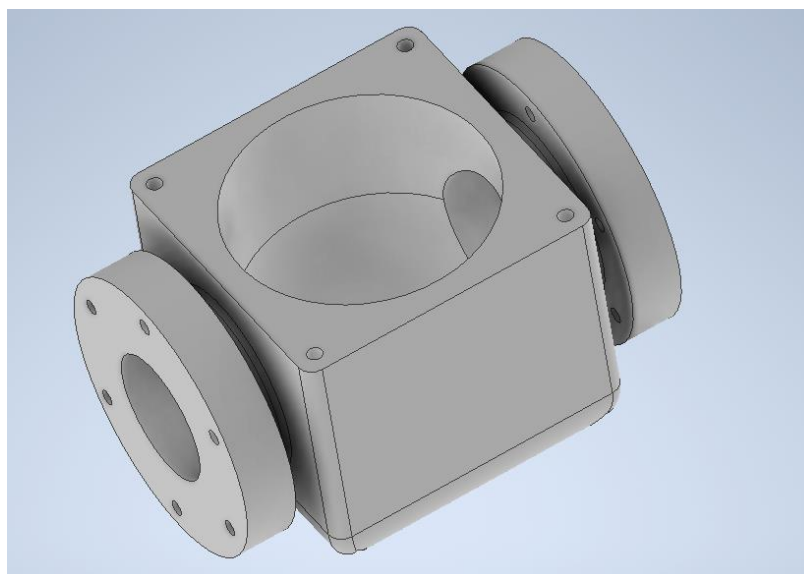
3Д модель корпуса мехатронного модуля контроля трубопровода.
